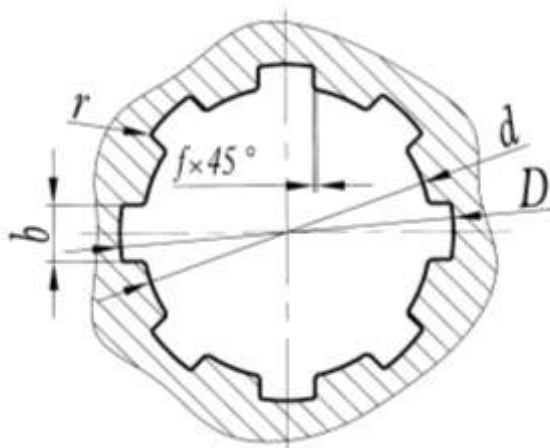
Зовнішній вигляд оброблюваної шліцьової втулки
